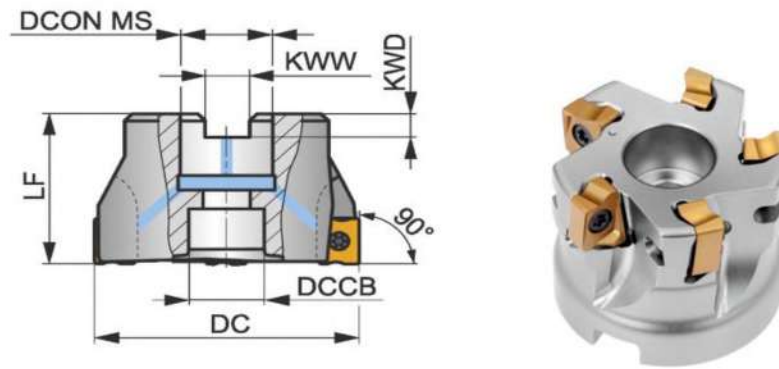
Торцева фреза 100A06R-S90LN12-C
